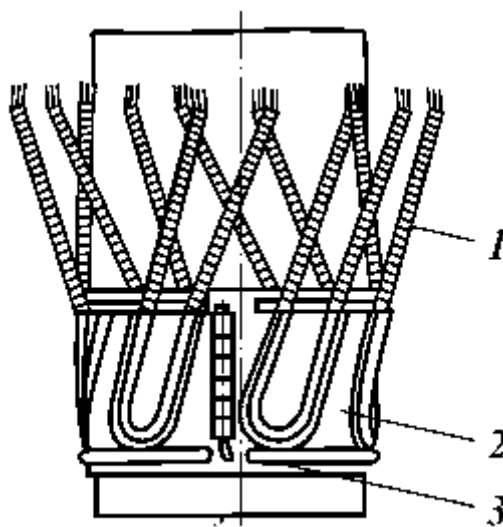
Скребок корончатого типа. 1-рабочий элемент; 2- корпус из двух полуколец; 3-соединительный штырь.
